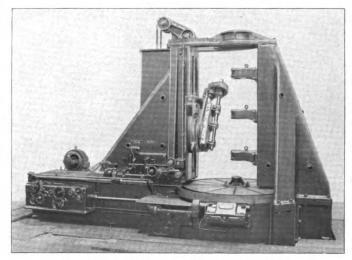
bis 6. Schraubenräder-Wälzfräsmaschine.
